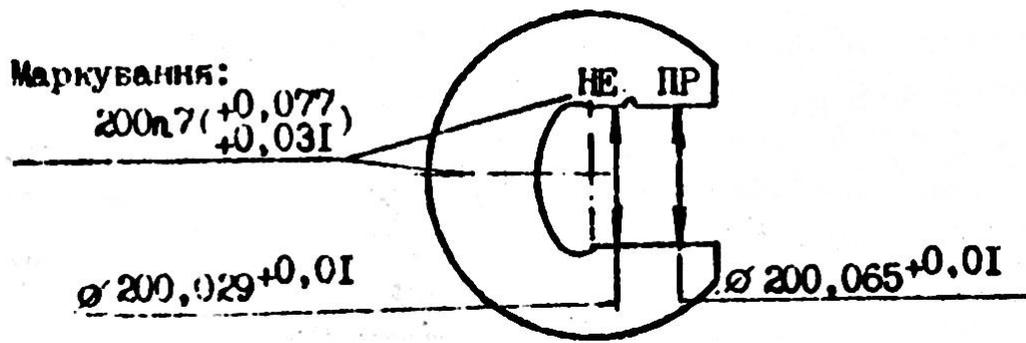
Калібр-скоба для контролю вала $\varnothing 200$ n7
